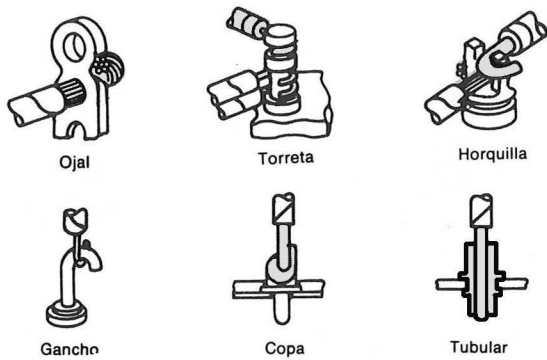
Fijación del conductor al borne antes de soldar.
